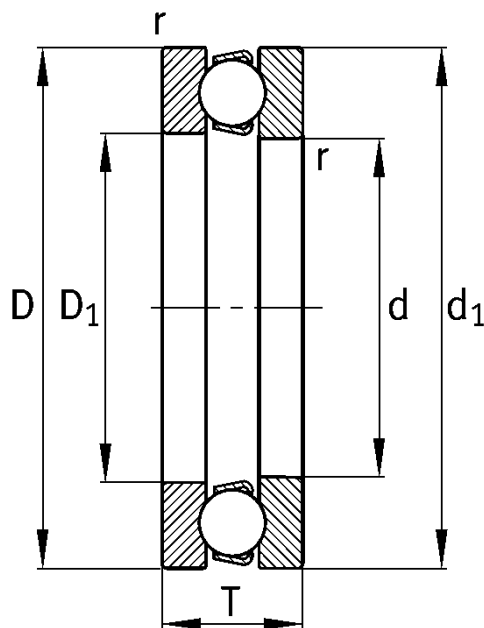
Габаритные размеры серии 511 ф. INA
